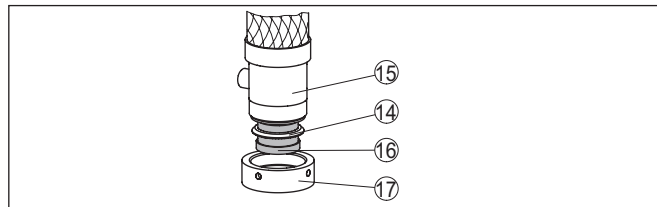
Montaje de la refrigeración de escintilador - parte inferior
